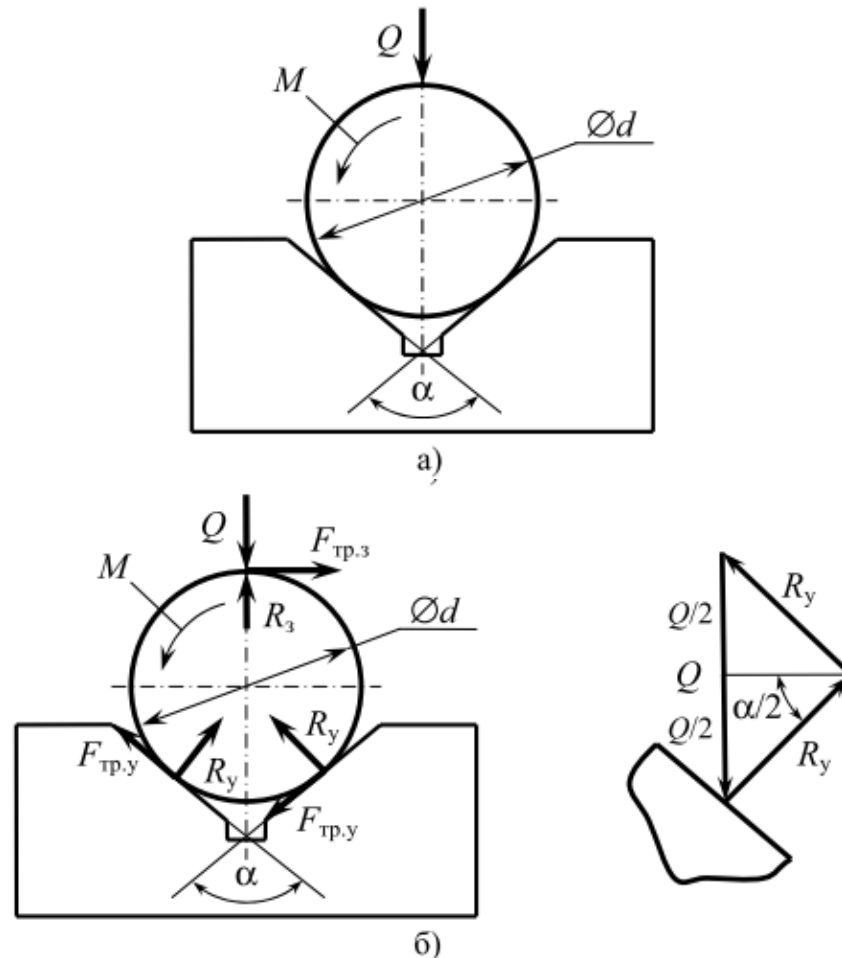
Исходная (а) и расчетная (б) схемы по определению требуемой силы закрепления заготовки при её установке в призму: α – угол призмы; Q – сила закрепления; M – момент сил резания, действующий на заготовку; R_y – реакция установочной поверхности призмы; R_3 – реакция поверхности зажимного элемента; $F_{тр.з}$ – сила трения по зажимному элементу; $F_{тр.у}$ – сила трения по установочному элементу
